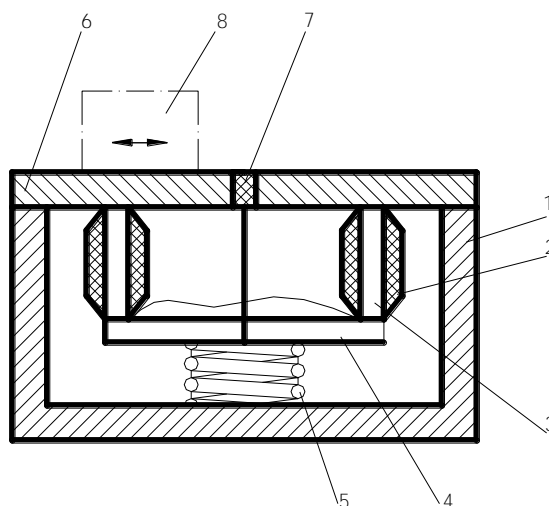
Схема работы демагнетизатора: 1 – корпус из немагнитного металла; 2 – катушки; 3 – сердечники; 4 – соединительная стальная планка; 5 – пружина; 6 – крышка; 7 – текстолитовая прокладка; 8 – деталь.
